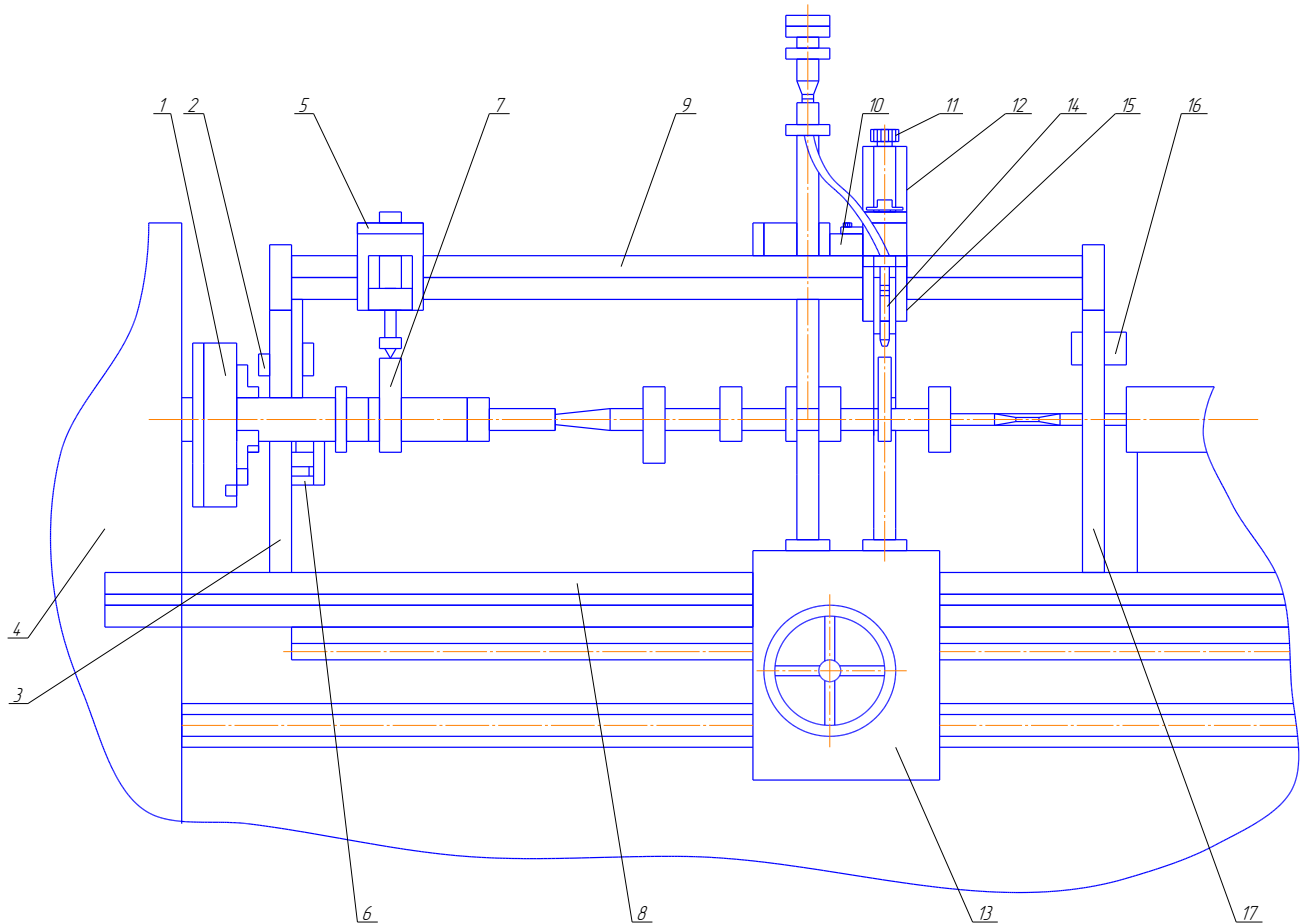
Загальний вигляд установки для плазмового наплавлення розподільного вала.
